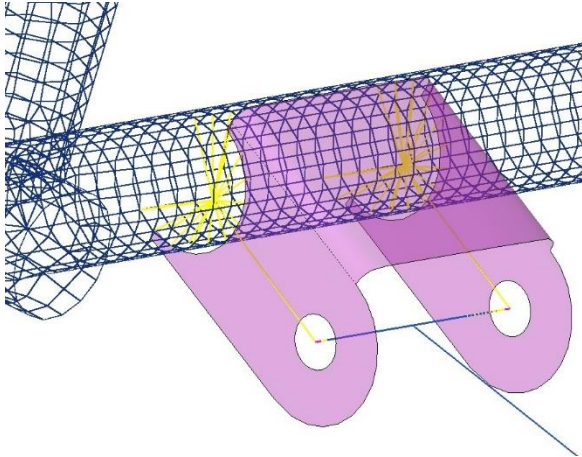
Junta revoluta. Soporte del chasis - brazo de control.
